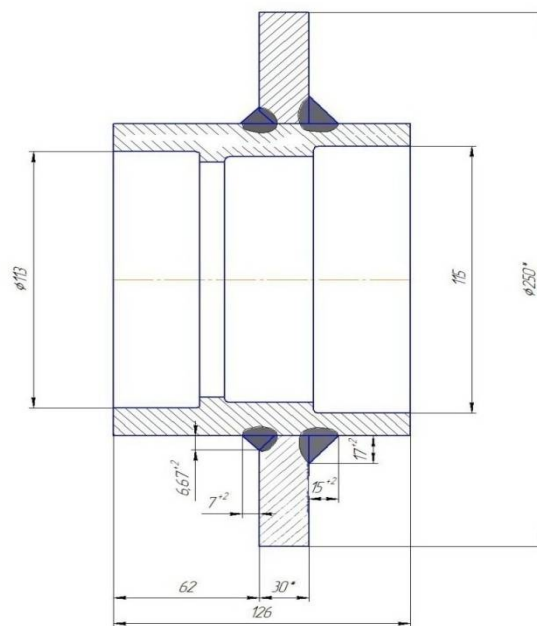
Заготовка деталі «Ступиця» (зварювальний варіант)
